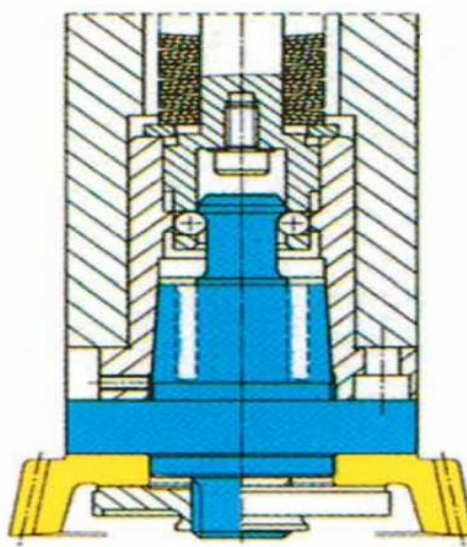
Odvalovací obrážka OHA 50 CNC 5 [21]
